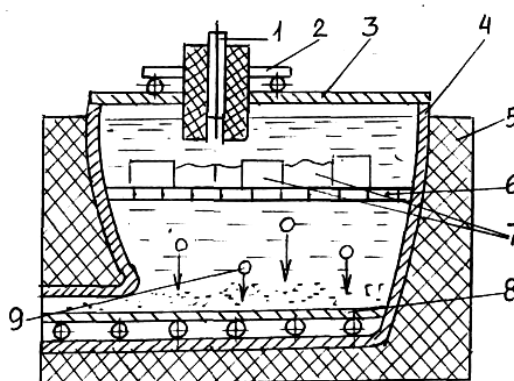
Схема устаткування для електрогідравлічного очищення ливарних деталей: 1 – електрод; 2 – візок; 3 – траверса; 4 – ванна; 5 – основа; 6 – решітка; 7 – заготовки (деталі); 8 – транспортер; 9 – осаджені частинки
